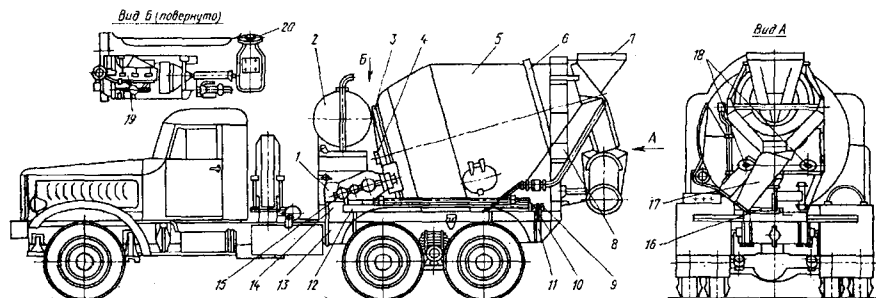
Автобетоносмеситель: 1 – рычаг управления декомпрессором; 2 – бак для воды; 3 – ведомая звездочка; 4 – главный подшипник барабана; 5 – смесительный барабан; 6 – бандаж; 7 – загрузочное устройство; 8 – лестница; 9 – рычаг управления муфтой сцепления; 10 – рычаг управления подачей топлива; 11 – рычаг управления реверсом редуктора; 12 – рама; 13 – шасси; 14 – контрольно-измерительная аппаратура; 15 – редуктор привода барабана; 16 – устройство для поворота лотка; 17 – лоток; 18 – опорные ролики; 19 – двигатель привода барабана; 20 – ведущая звездочка.
